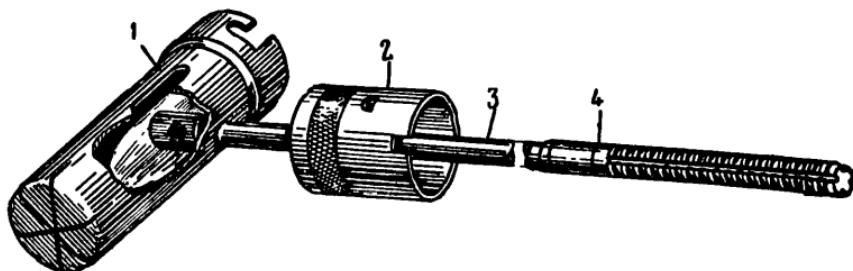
Принадлежность автомата, подготовленная для чистки ствола:
